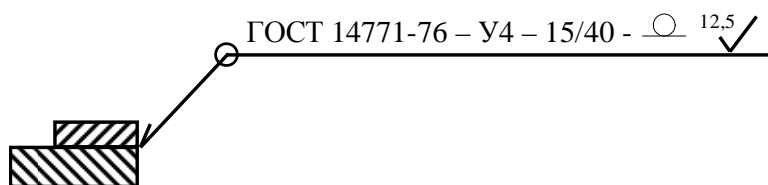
Пример условного обозначения стандартного сварного шва
